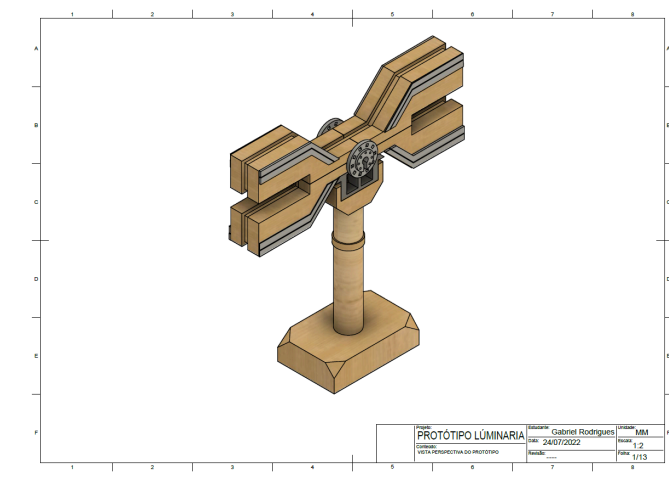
Vista perspectiva de desenho técnico do protótipo.
